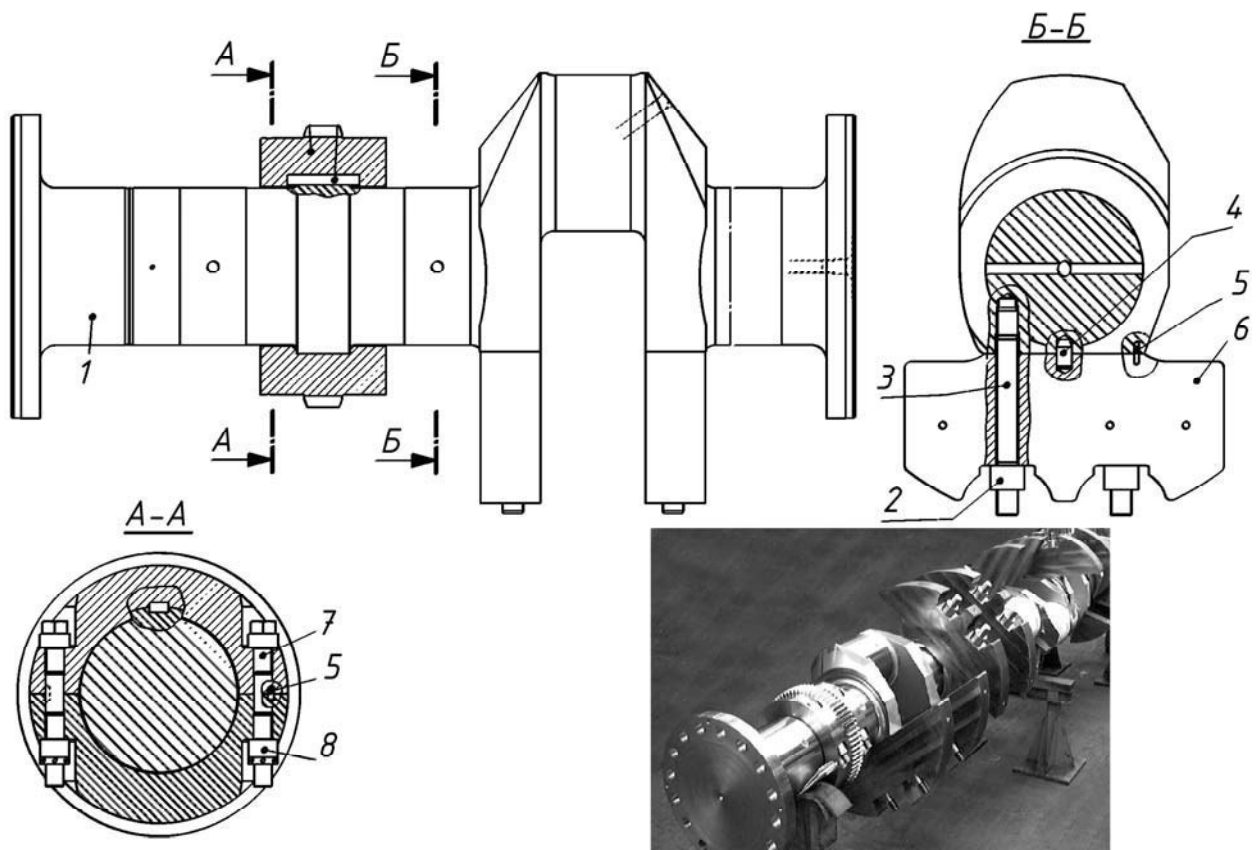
Колінчатий вал з противагами: 1 – носок; 2 – гайка кріплення противаги; 3 – шпилька кріплення противаги; 4, 5 – штифт; 6 – противага; 7 – гайка кріплення шестерні приводу допоміжних механізмів; 8 – шпилька кріплення шестерні приводу допоміжних механізмів
